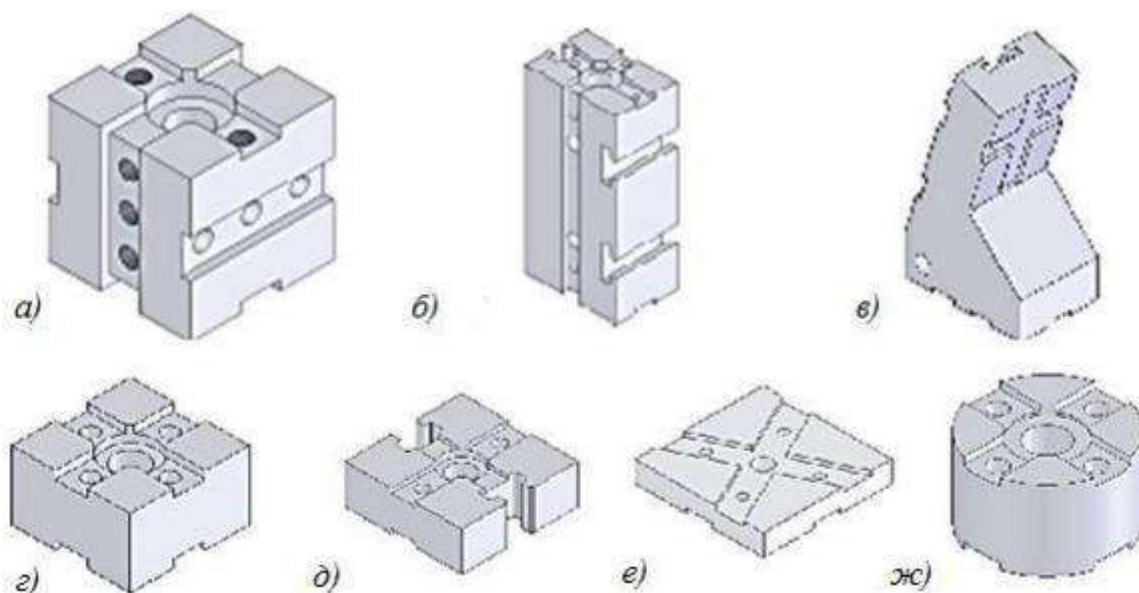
Корпусные детали: а) опора квадратная, б) опора прямоугольная, в) опора угловая, г),д),е) прокладки прямоугольные, ж) прокладка круглая.
